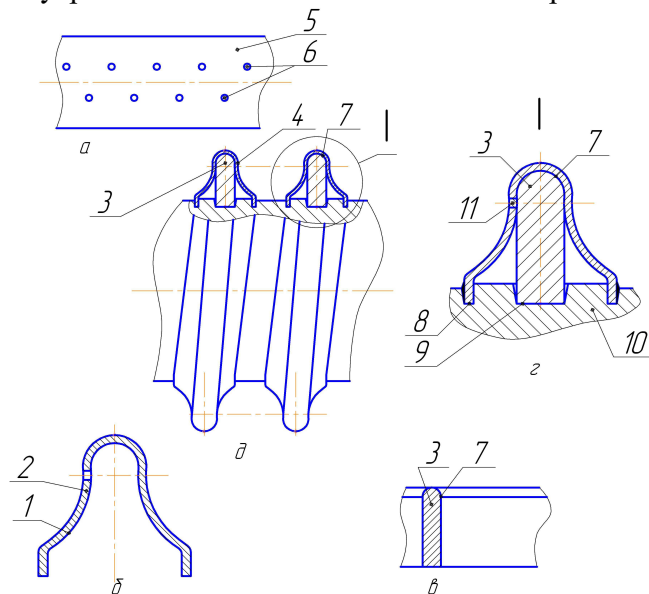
Гвинтові спіралі підвищеної міцності верстаті 16К20 або ДИП-200 чи ДИП-300 в залежності від розмірів спіралей і зусилля - формоутворення, зварювання деталей здійснюється в разі потреби зварювальною контактною машиною.
